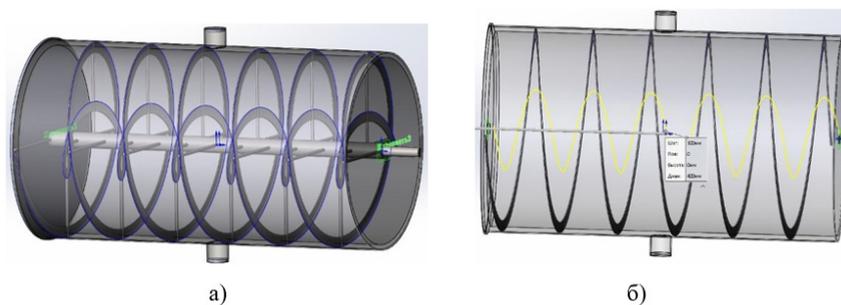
Цифровая модель ленточного смесителя с цилиндрической камерой:
